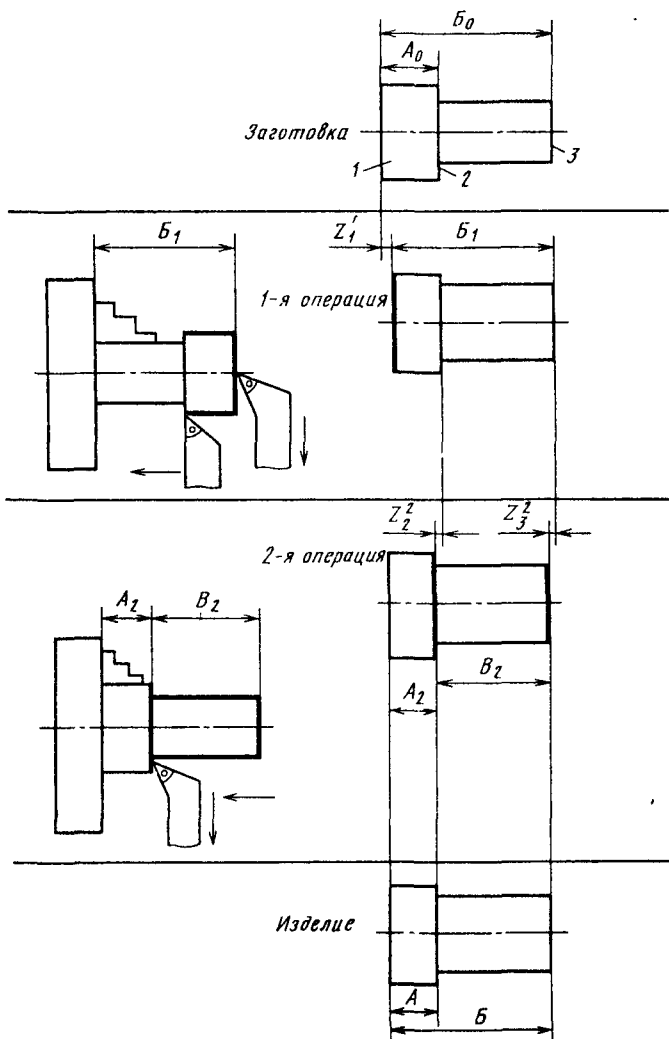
Схема преобразования размеров заготовки в процессе изготовления детали. Поверхности заготовки нумеруют слева направо цифрами 1, 2, 3 и т.д. и далее к номеру поверхности добавляют нули. Поверхности заготовки 10, 20, 30 обозначают точками, от них проводят вертикали. В зоне с надписью "Заготовка" наносят размеры заготовки A_0 и B_0 , которые, как и поверхности, имеют нулевые индексы, что указывает на принадлежность к размерам заготовки.
